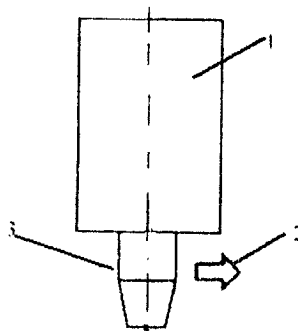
Схематичне зображення MJS-способу: 1 – камера розтоплення; 2 – рух; 3 – зміна системи форсунки
